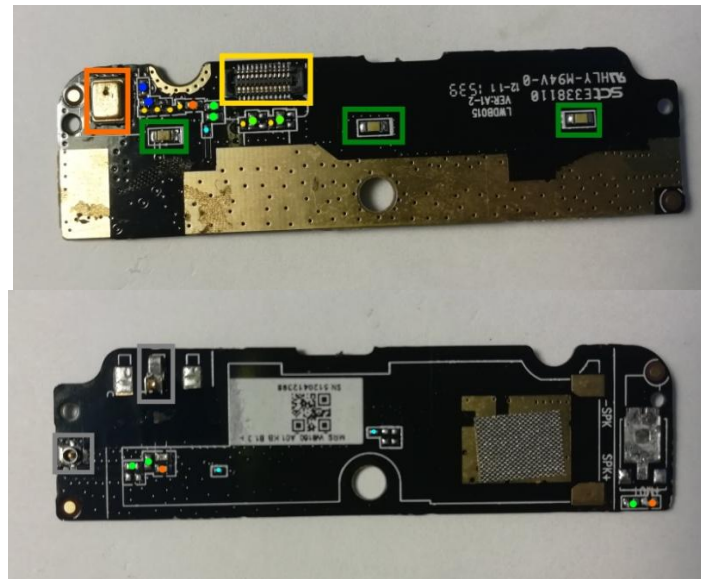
PCB inferior con los componentes identificados marcados en color, nótese que el motor vibrador fue desoldado para su medición por separado.
